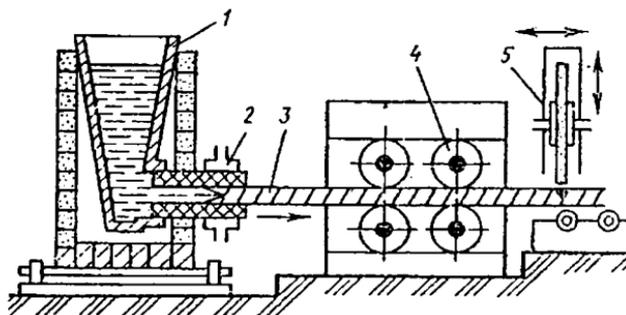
Установка горизонтального типа для непрерывного литья: 1 — металлоприемник; 2 — кристаллизатор; 3 — заготовка; 4 — тянущее устройство; 5 — устройство резки
